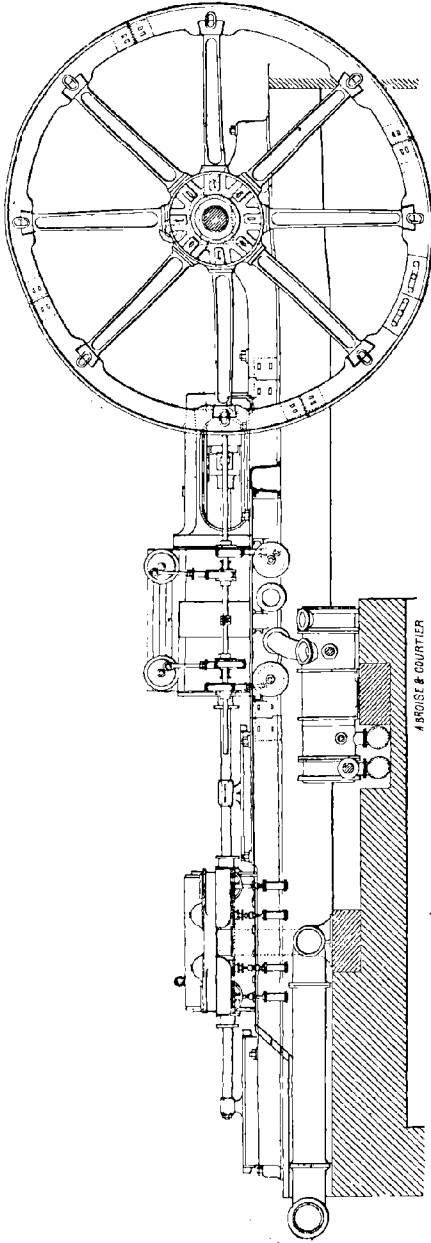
Machine soufflante Riedler, à Heft (Carinthie) (élévation).
